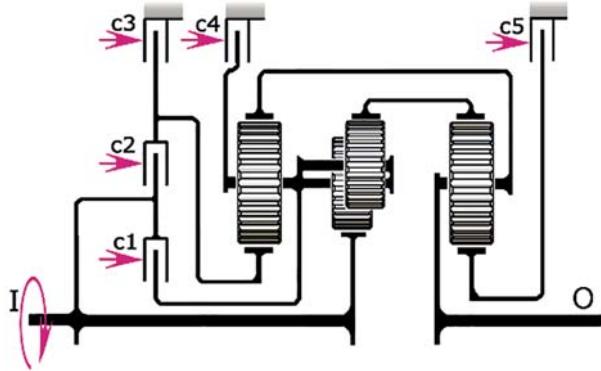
Кинематическая схема 6-ти ступенчатой планетарной коробки передач фирмы ООО «КАТЕ»:
